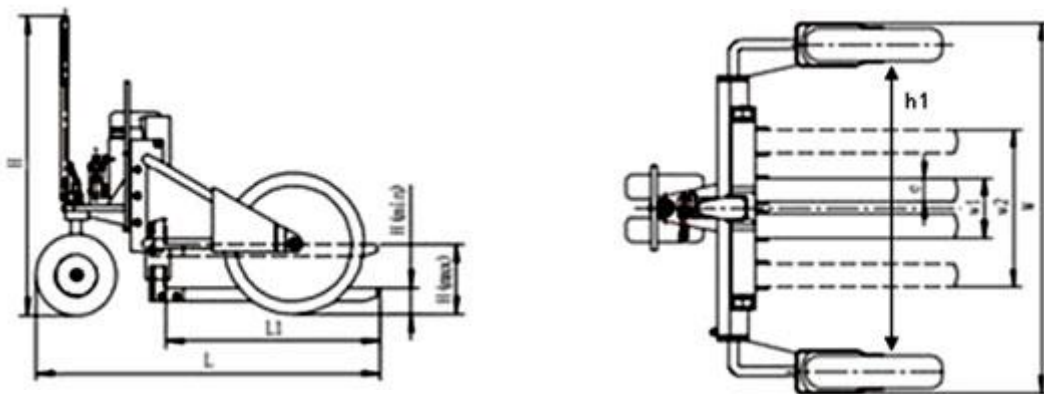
Габаритные размеры тележка для бездорожья HW.
